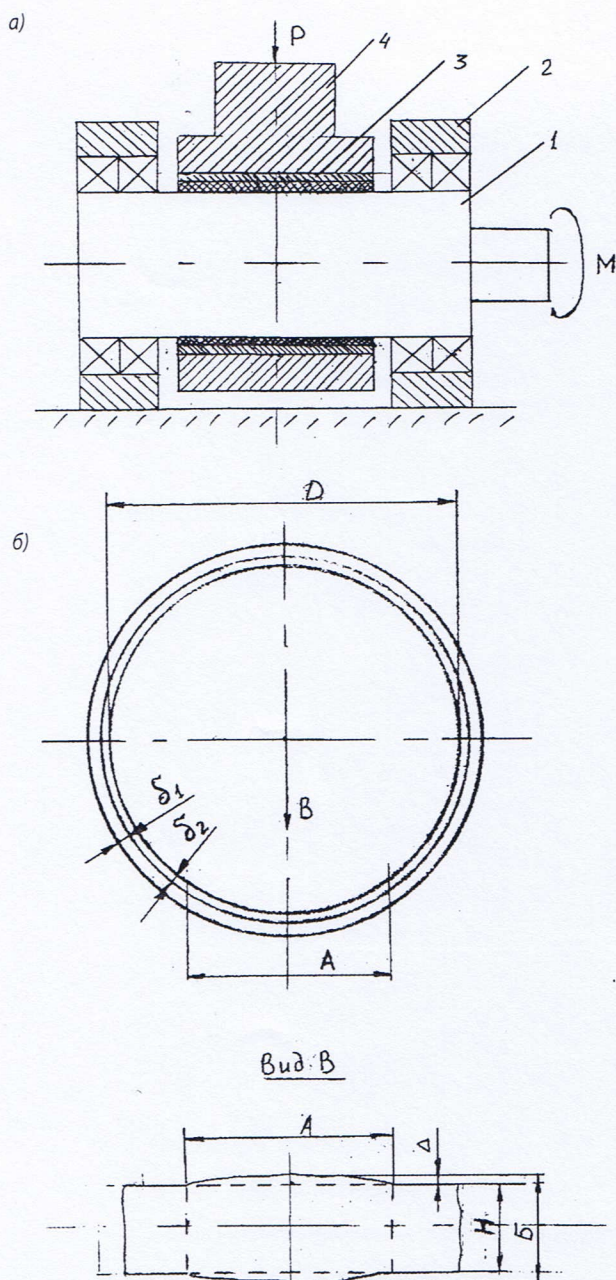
а) схема установки для определения несущей способности металлофторопластовых подшипников скольжения; б) чертеж подшипника и схема определения зоны пластической деформации
